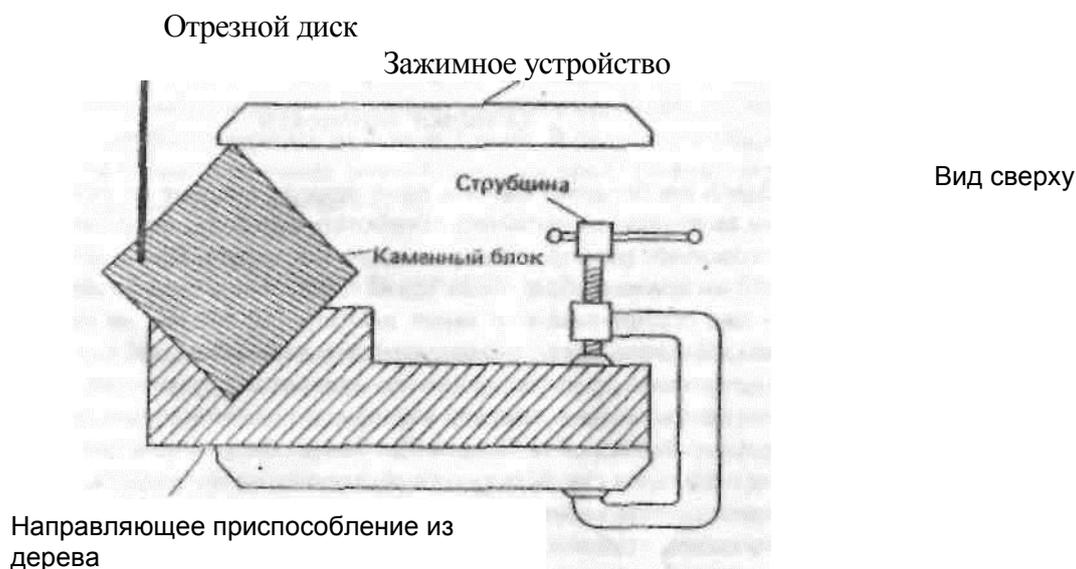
Деревянный кондуктор для отпиливания заготовок шаров.
